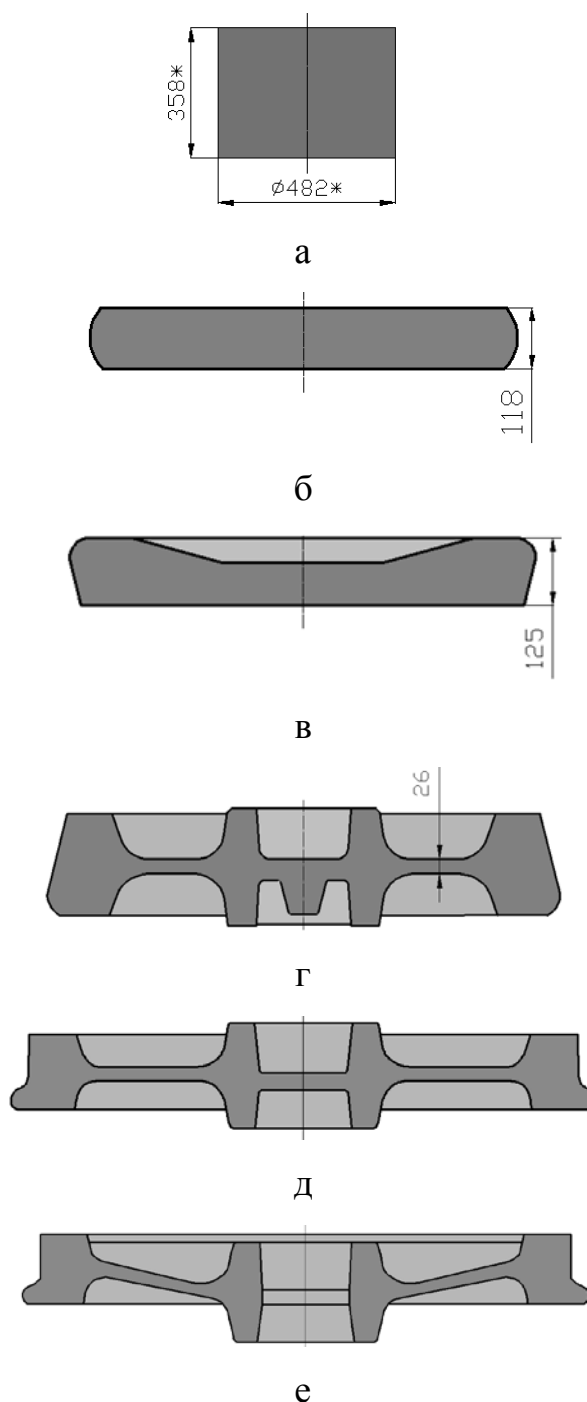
Схема деформации заготовки на прессо- прокатной линии АО «ВМЗ»: а - исходная заготовка, б- свободная осадка (пресс 19,6 МН), в-
